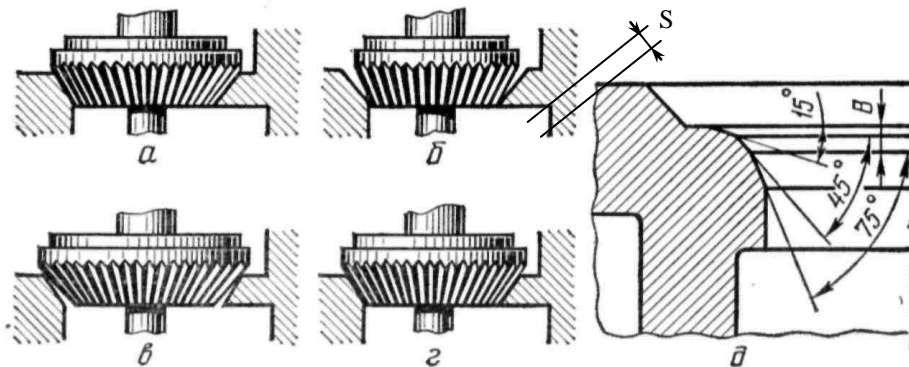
Ремонт клапанных гнезд фрезерованием: а - фрезой черновой 45° ; б - фрезой черновой 75° ; в - фрезой черновой 15° ; г - фрезой чистовой 45° ; д - схема образования рабочей фаски гнезда при фрезеровании; В - ширина рабочей фаски.
